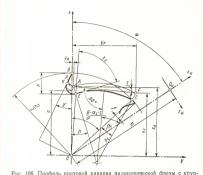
Профиль винтовой канавки цилиндрической фрезы с крупным зубом
